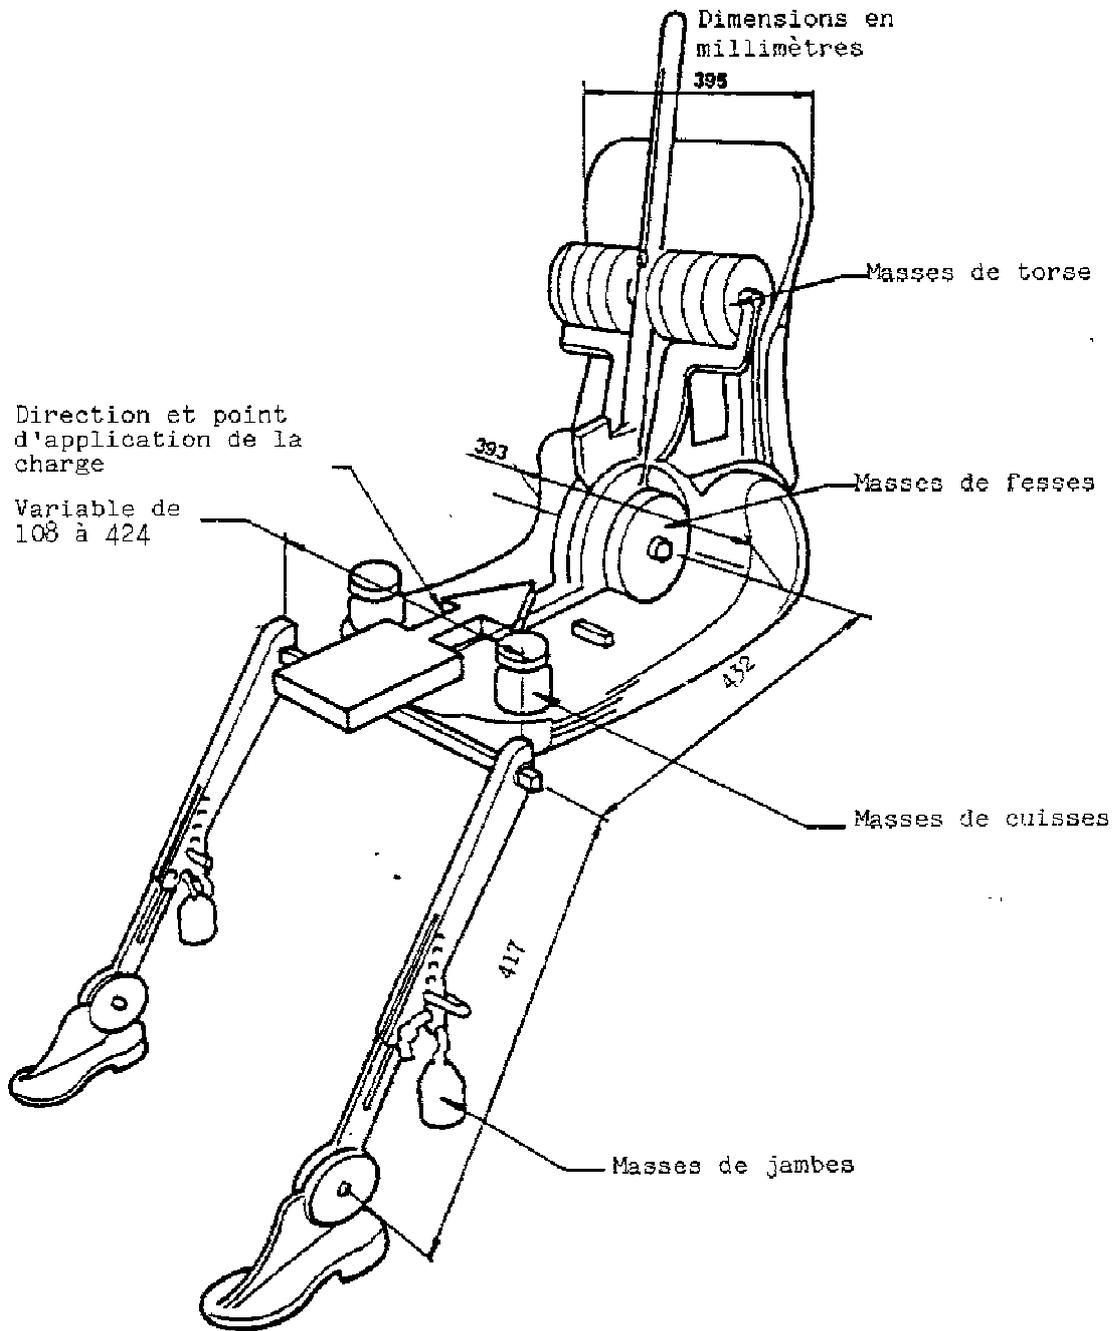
Dimensions des éléments de la machine 3-D H et emplacement des masses
